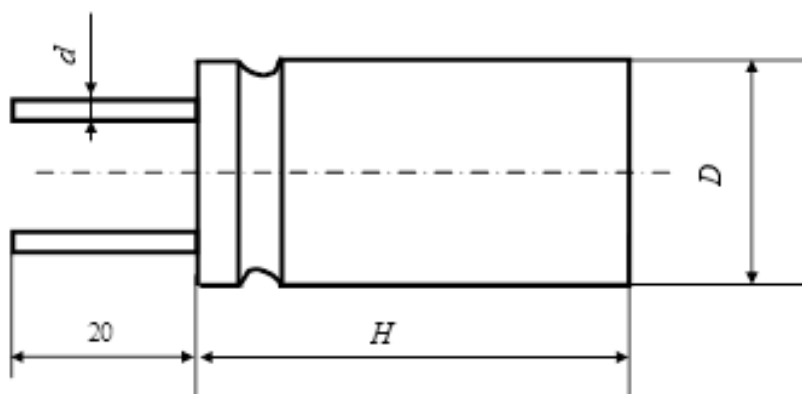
Внешний вид и габаритные размеры электролитического конденсатора К50-16
